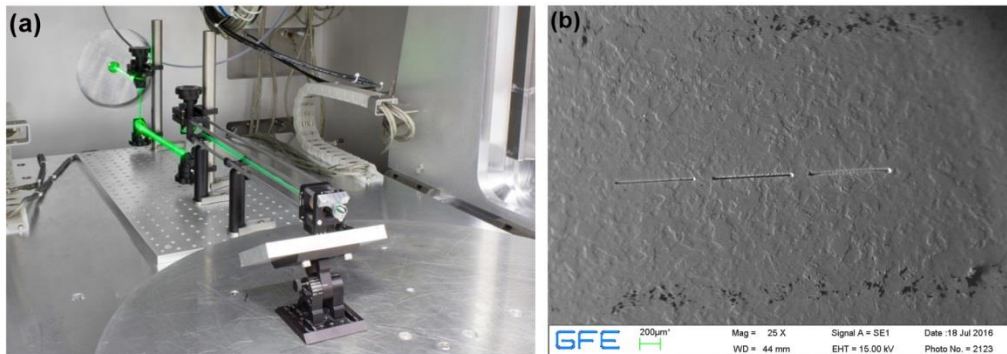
Aufbau einer Versuchsanlage zum Laserstrahlschweißen.
